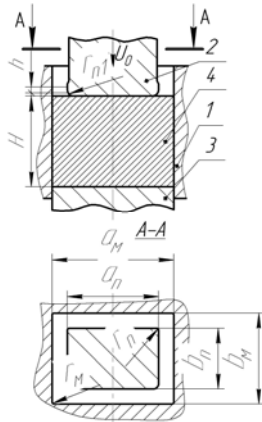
Схема зворотного видавлювання коробчатих виробів
